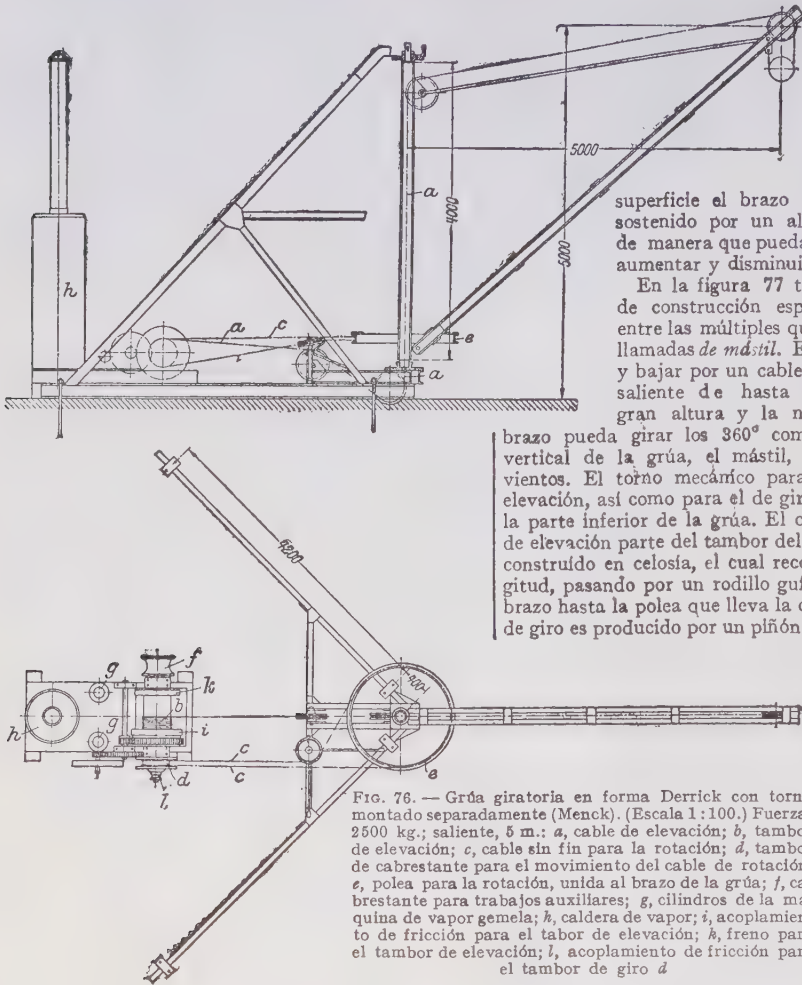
Grúa giratoria en forma Derrick con torno montado separadamente (Menck). (Escala 1:100.) Fuerza, 2500 kg.; saliente, 5 m.: a, cable de elevación; b, tambor de elevación; c, cable sin fin para la rotación; d, tambor de cabrestante para el movimiento del cable de rotación; e, polea para la rotación, unida al brazo de la grúa; f, cabrestante para trabajos auxiliares; g, cilindros de la máquina de vapor gemela; h, caldera de vapor; i, acoplamiento de fricción para el tabor de elevación; k, freno para el tambor de elevación; l, acoplamiento de fricción para el tambor de giro d
